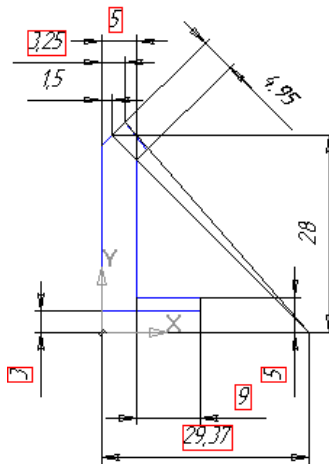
Ескіз заготовки зубчастого колеса
